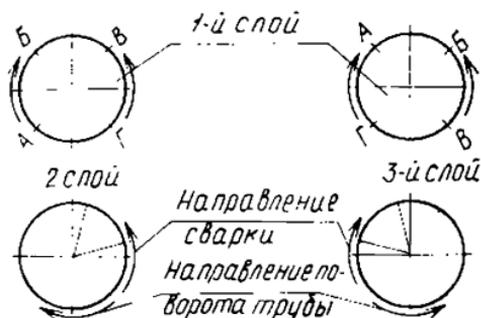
Схема наложения слоев шва при ручной электродуговой сварке поворотных стыков
